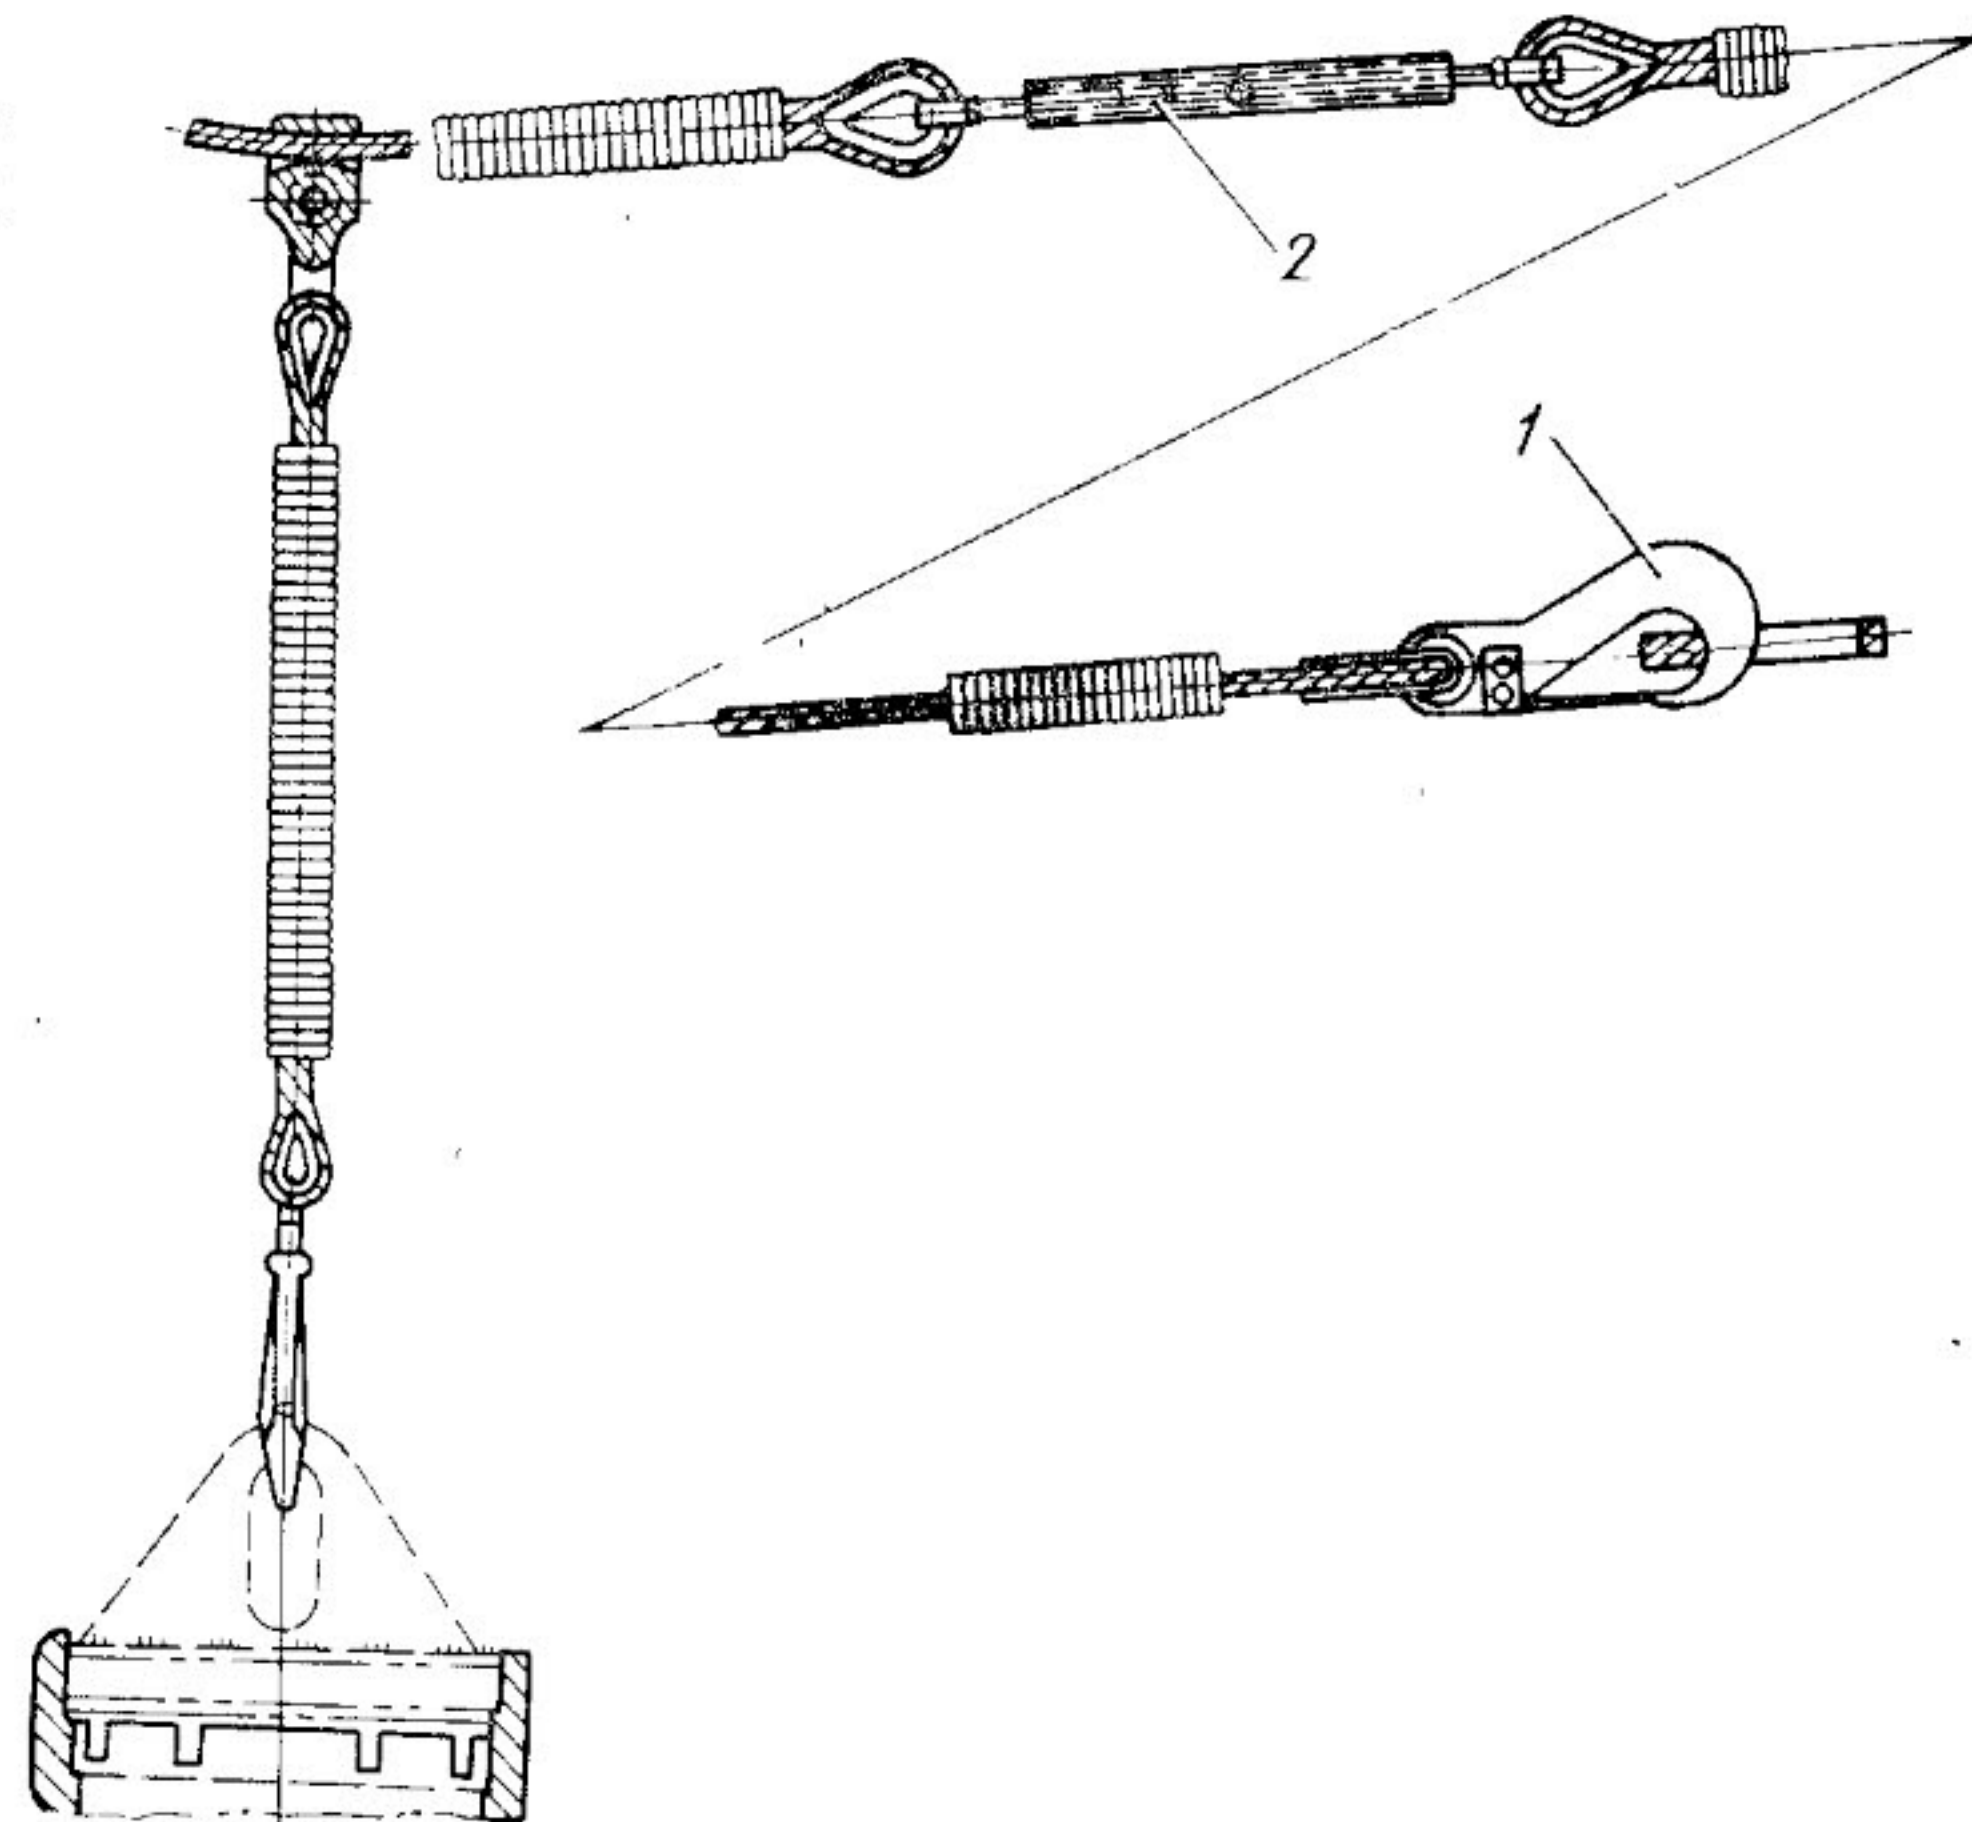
Монтаж приспособления для швартовки хвостового винта:
